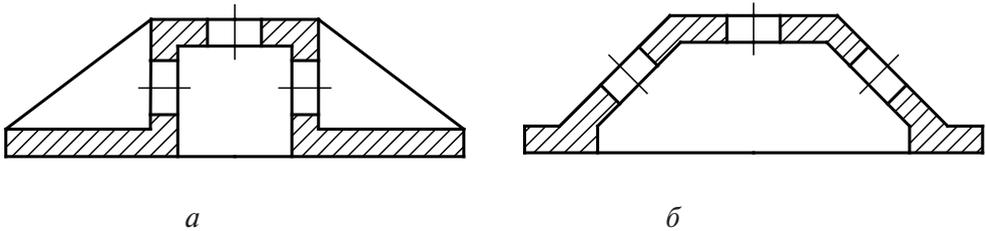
Конструкция корпусных деталей с отверстиями:
